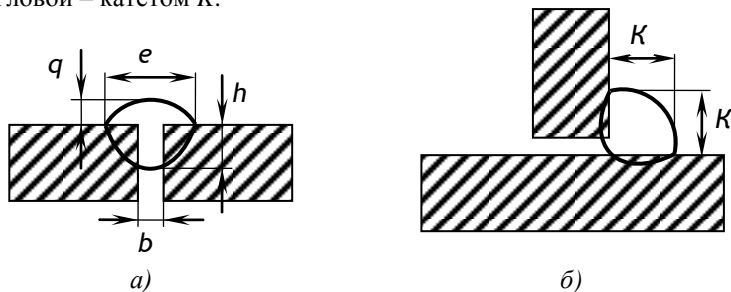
Геометрические параметры сварных швов, где а – стыковой, б – угловой
